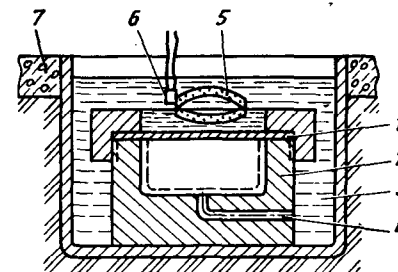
Схема штамповки деталей горючими газовыми смесями с передачей давления на заготовку жидкостью:
